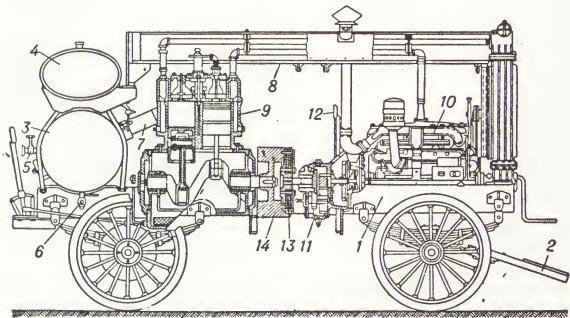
Передвижная компрессорная станция с двигателем внутреннего сгорания, смонтированная на прицепной тележке: 1 — рама; 2 — дышло; 3 — ресивер; 4 — бак для горючего; 5 — воздухохранильный кран; 6 — продувной кран; 7 — нагнетательный патрубок; 8 — крыша; 9 — компрессор; 10 — двигатель (автомобильный); 11 — редуктор; 12 — рычаг включения; 13 — муфта включения; 14 — маховик.
